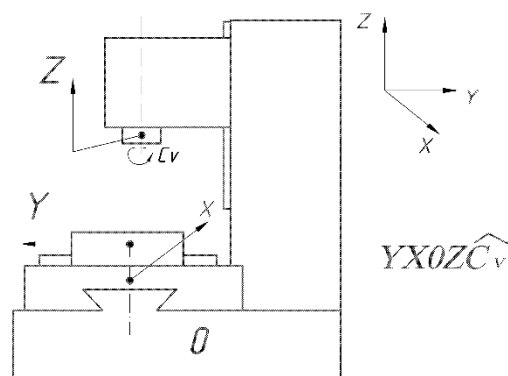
Варіант компоновки вертикально-фрезерного верстату
